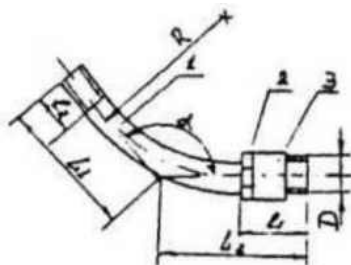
Нормализованный трубный угловой элемент 135°
